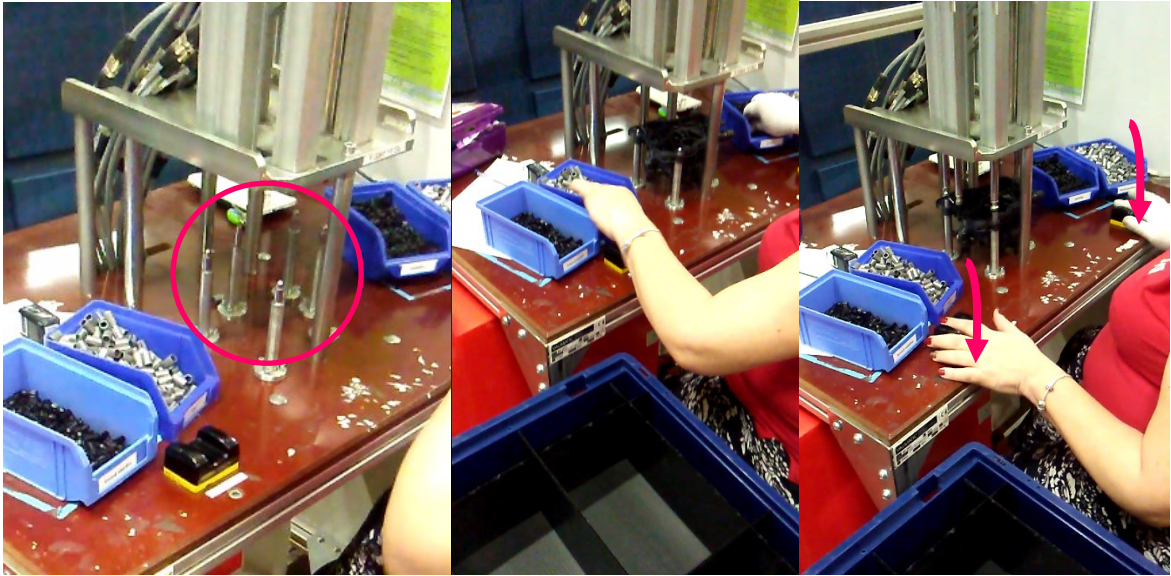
a 27 Hot stamping – zalisování mosazné vložky (vlastní zpracování)
